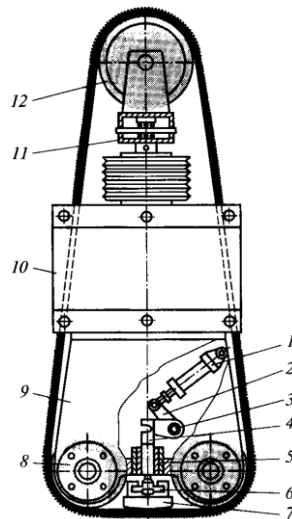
Шліфувальний агрегат з контактною балкою: 1 – пневмоциліндр; 2 – важіль; 3 – вал; 4 – шток; 5 – втулка; 6 – напрямна; 7 – утюжок; 8 – приводний ролик; 9 – кронштейн; 10 – траверса; 11 – механізм натягу; 12 – натяжний ролик
